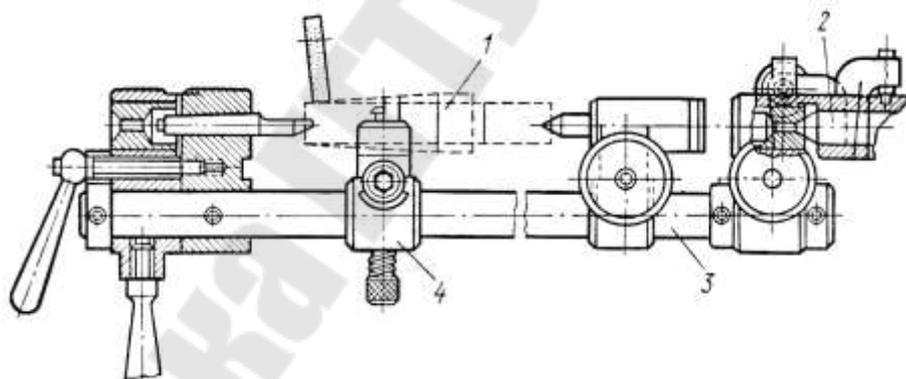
Делительное приспособления для конической заточки задней поверхности режущей части метчика: 1 – метчик; 2 – центр станка; 3 – штанга; 4 – упорка.
